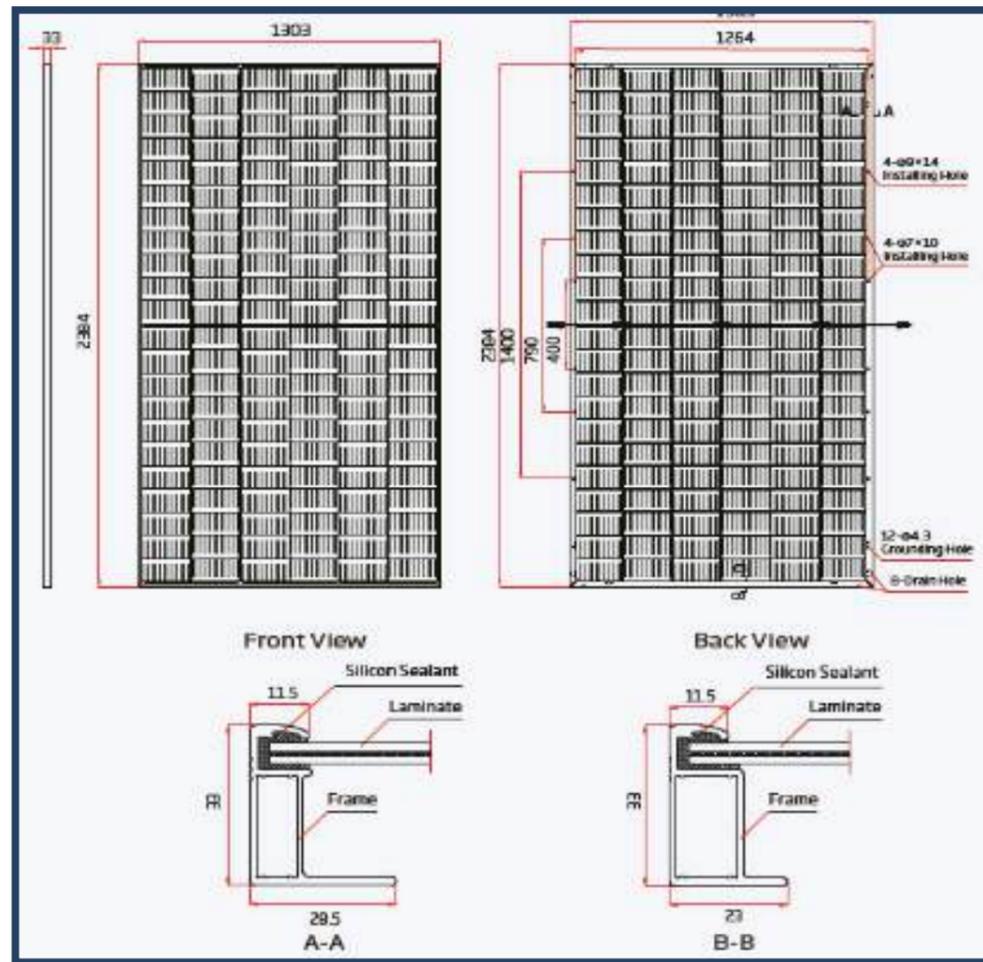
Dimensions et vue d'un panneau photovoltaïque
